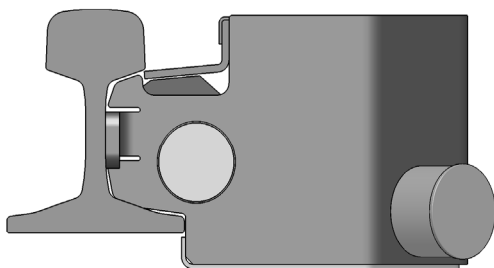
Type SK420-012 (Schienenprofil S49; geschraubt/geschweißt)
